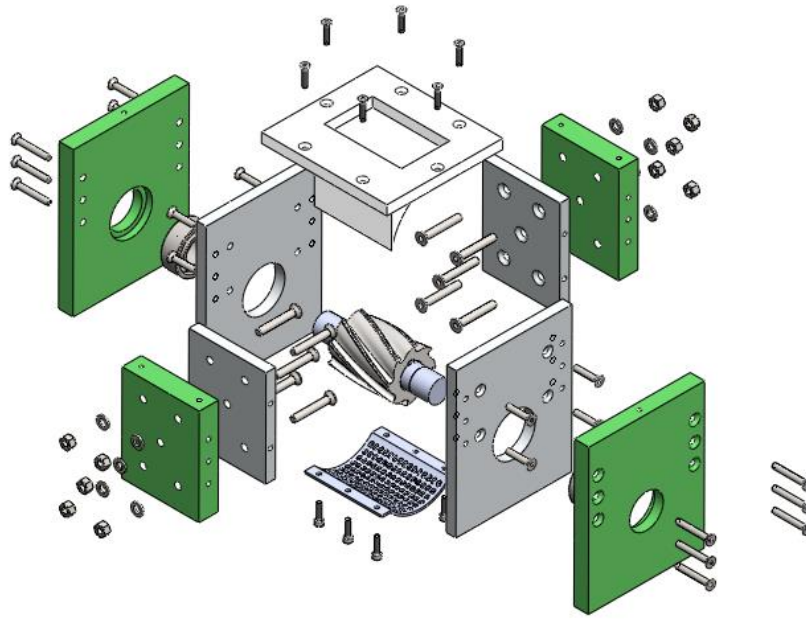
Conjunto explosionado (Detalle estructuras plástico) [Fuente propia]
